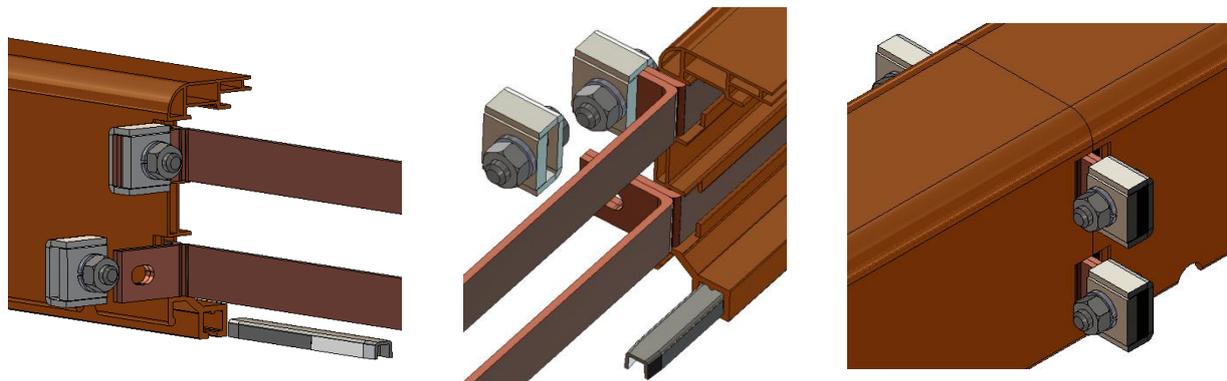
Сборка выравнивающих пластин и стыковочных хомутов
